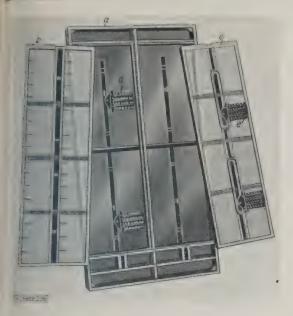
Zweiteiliger Siebrahmen für Großplansichter mit geteiltem Bürstenlauf.
